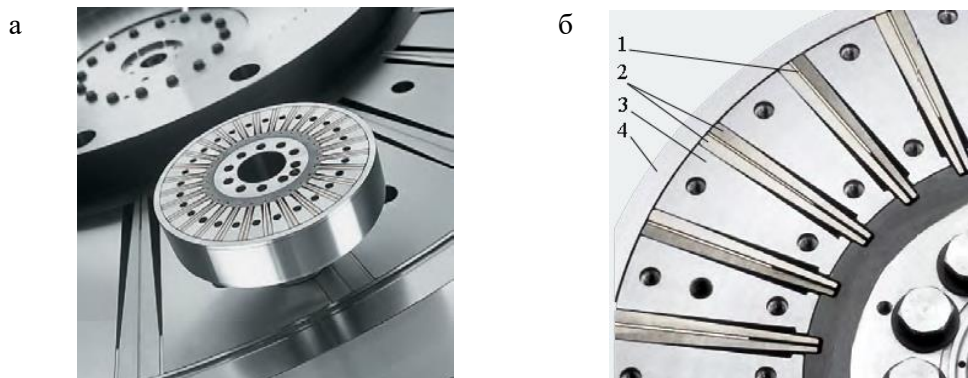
Пружинный демпфер крутильных колебаний «Geislinger» [9]: а – общий вид, б – конструкция; 1 – промежуточная вставка между рессорными пружинами, 2 – рессорные пружины, 3 – сектор маховой массы, 4 – внешний обод (корпус) демпфера
